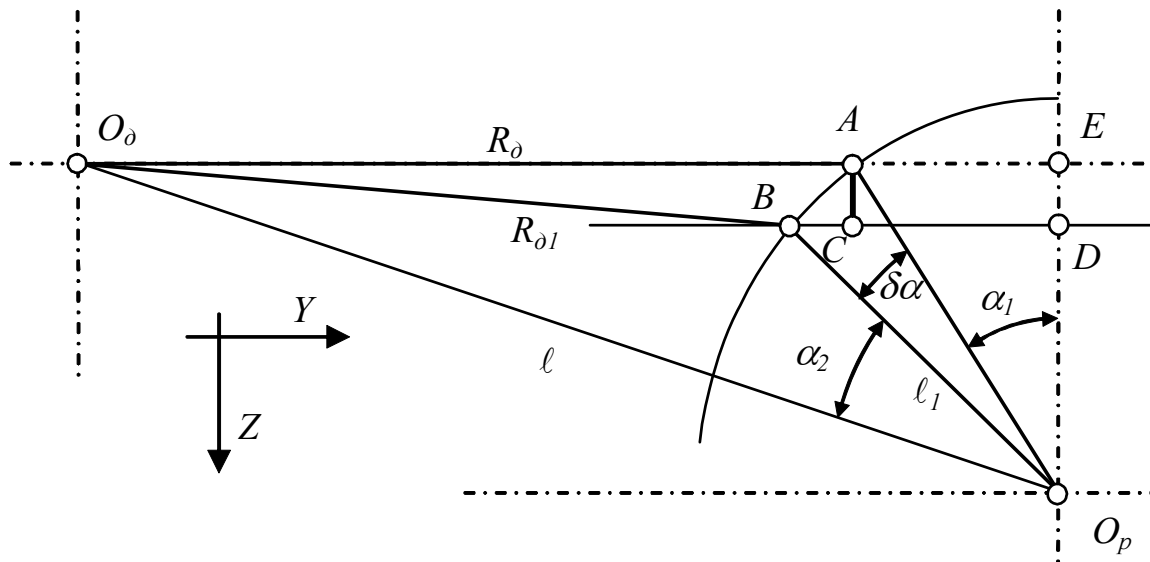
Розрахункова схема компенсації похибки обробки
